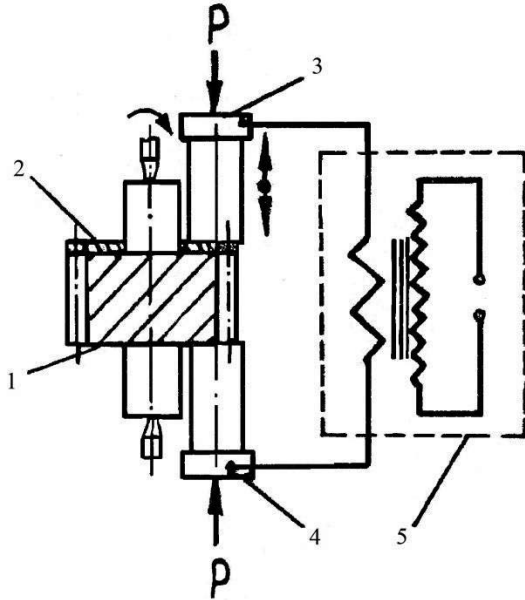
Схема приварювання зубчастої пластини до торця шестерні гідронасоса: 1 – шестерня; 2 – пластина; 3 – верхній підвісний електрод; 4 – нижній нерухомий електрод; 5 – джерело струму
